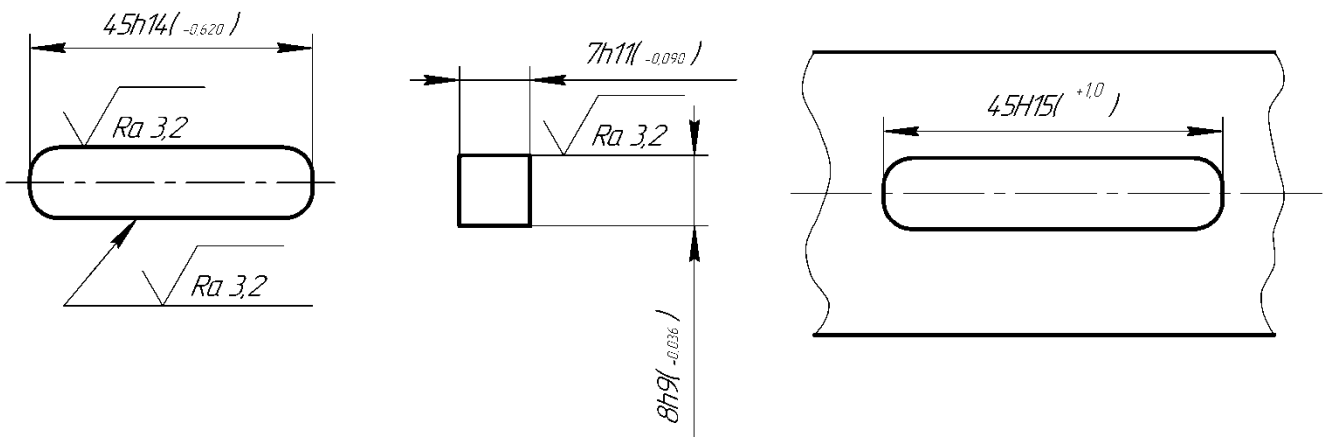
Обозначение допусков размеров деталей шпоночного соединения
